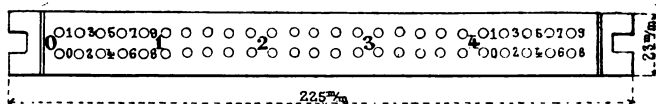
Vue de face d'une réglette de 50 jacks.
